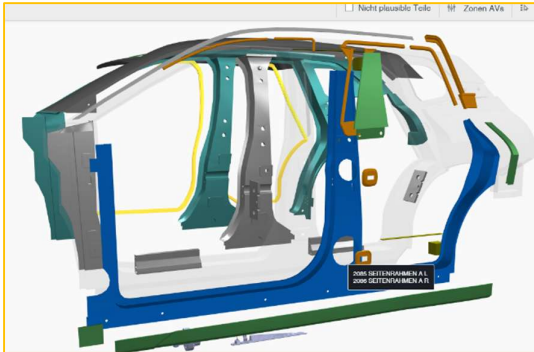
+19: Auszug aus Audatex Capter Grafik, links Seitenrahmen Carbon, rechts Seitenteil hinten mit Abdeckung Wasserrinne bzw. Blende Heckleuchte ohne Hinweise
